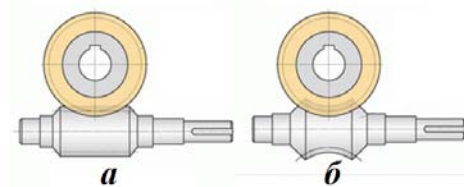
Типи черв'яків: а – циліндричний; б - глобоїдний
